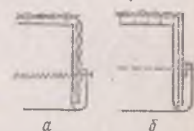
Обработка низа отлетной подкладки в изделиях с утепляющей прокладкой
